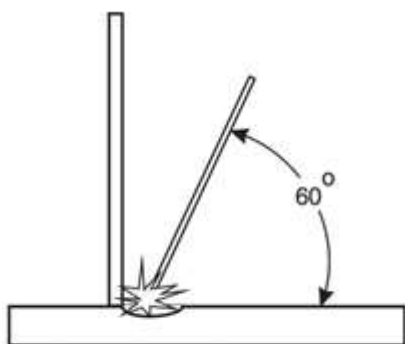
Сварка тонкого с более толстым металлом.
